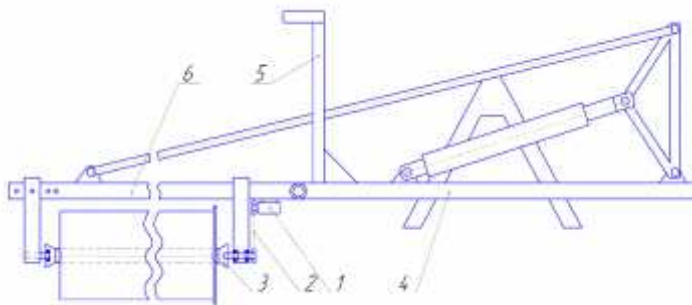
Приспособление для разматывания рулона укрывочного материала
